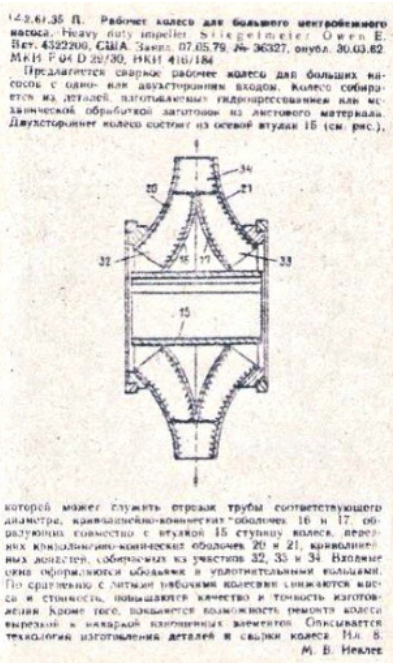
Рабочее колесо сварной конструкции для крупного центробежного насоса двустороннего входа
